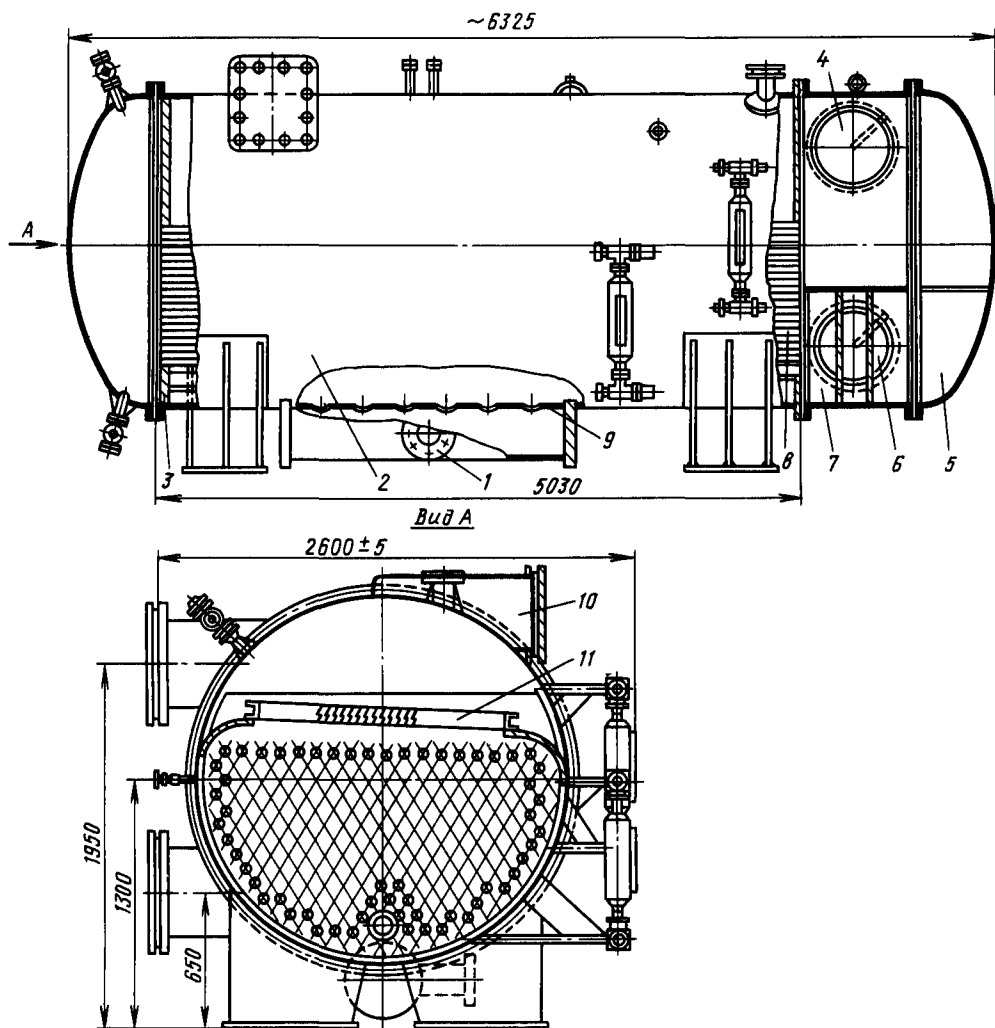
Фреоновый кожухотрубный испаритель затопленного типа для турбокомпрессорного агрегата:
